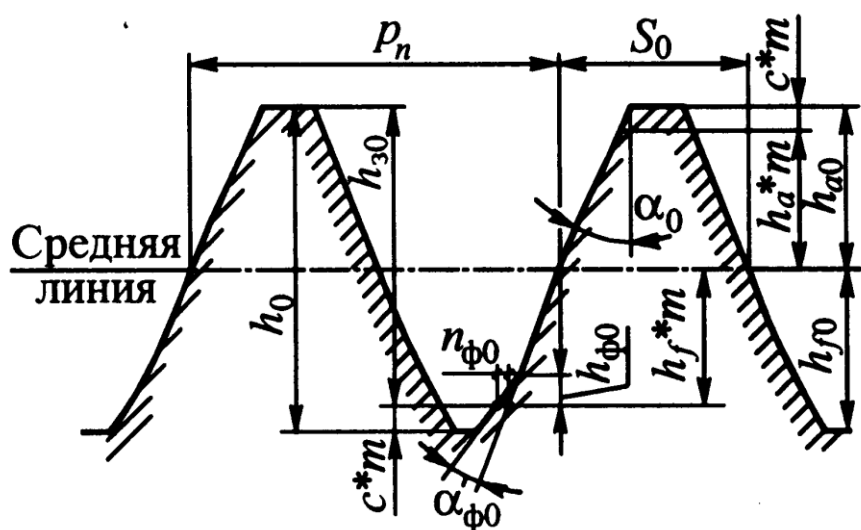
Исходный контур инструментальной рейки для эвольвентных зубчатых колес
